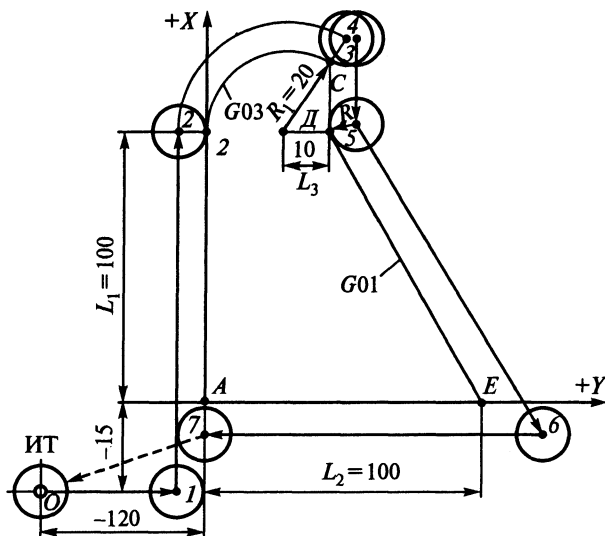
Схема обработки заготовки на фрезерном станке с ЧПУ:
